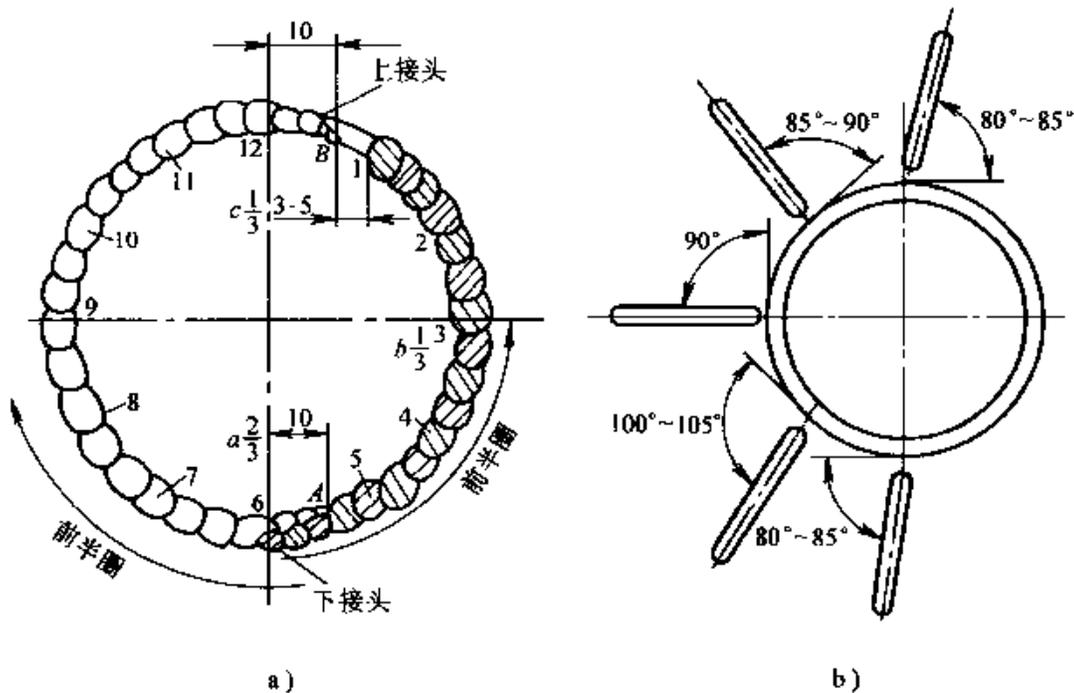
水平固定管子的焊接顺序及焊条角度
